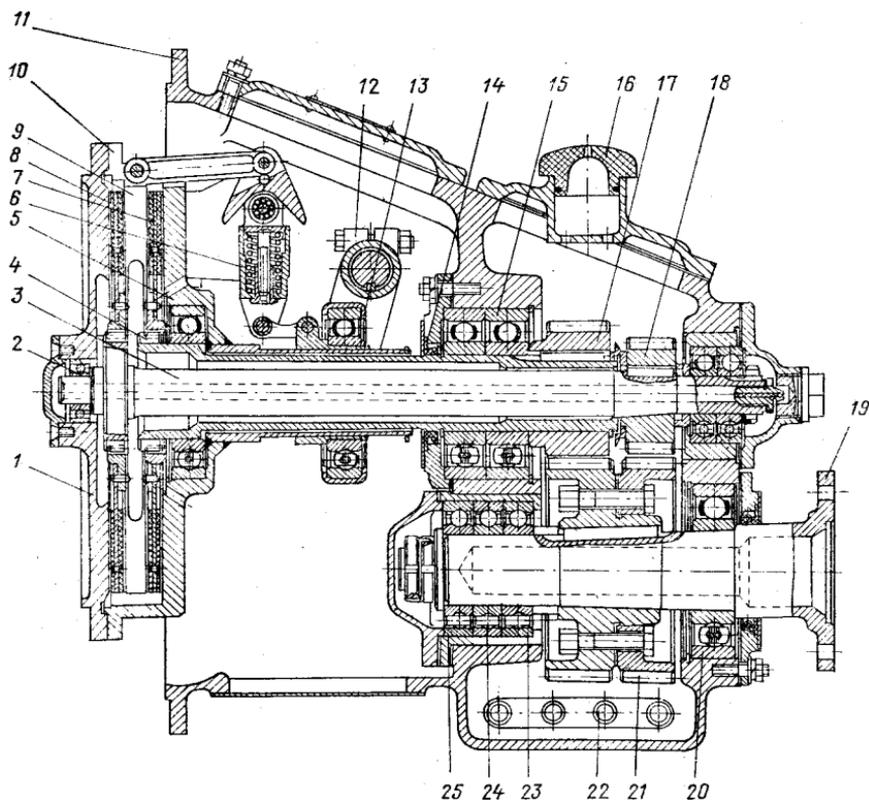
Продольный разрез реверсредуктора РРП-20.
